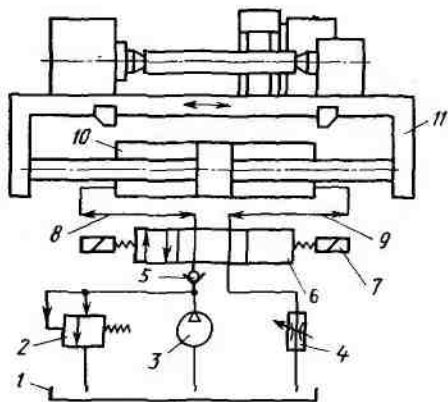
Схема гидравлического привода стола круглошлифовального станка
